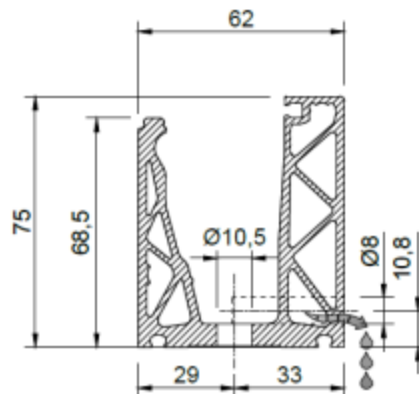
section transversale du profilé DFP88.60 avec indication de perçage pour drainage
